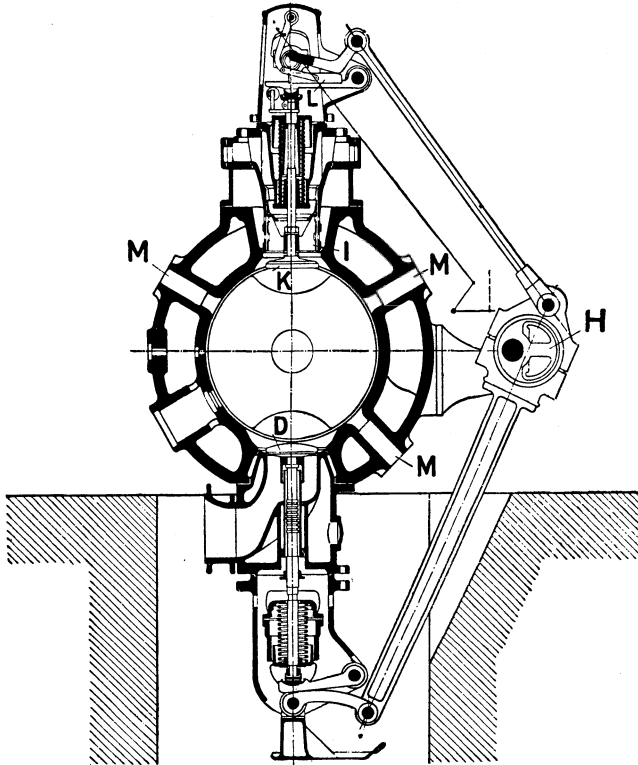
Zylinderquerschnitt zu Fig. 228.
